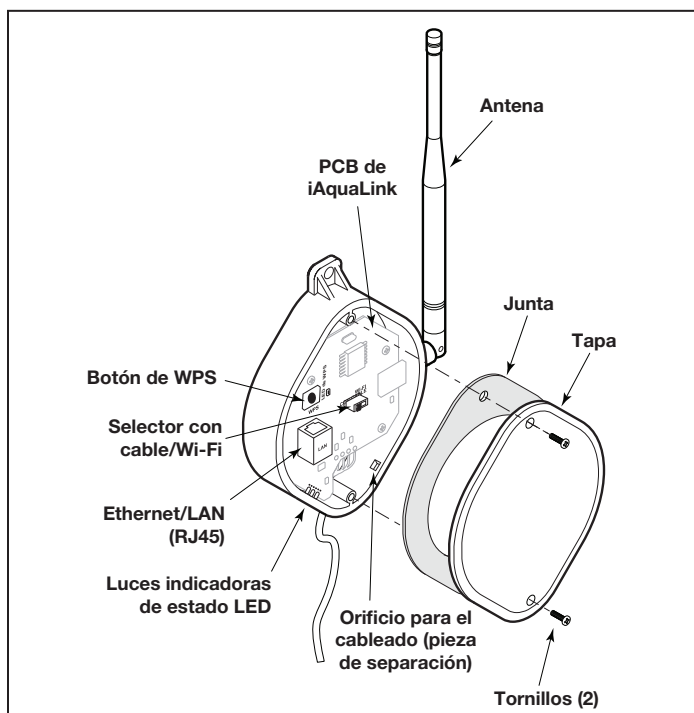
Componentes de la PCB del dispositivo iAquaLink
